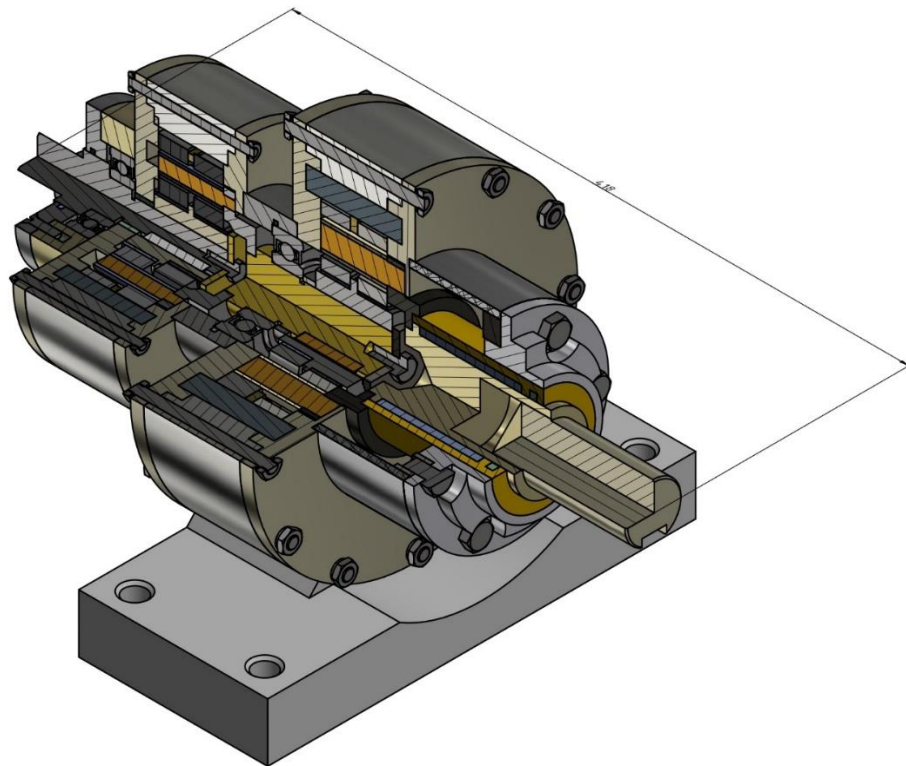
CAD-модель 2-х ступінчатого планетарно-цвнкового редуктора.
